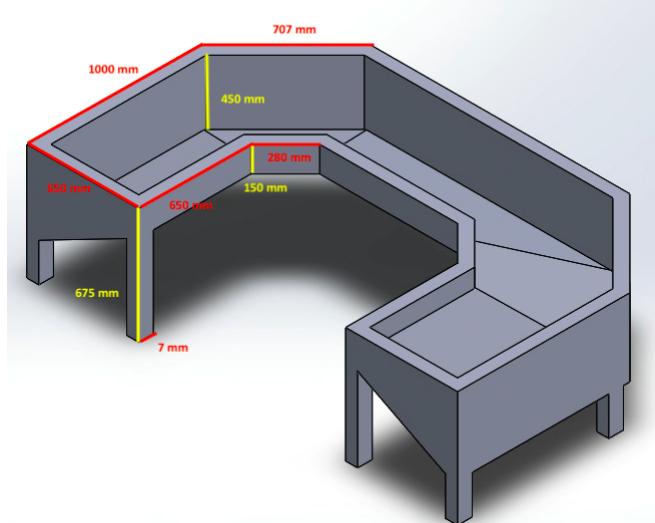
Dimensions de la jardinière conçue sur Solidworks
